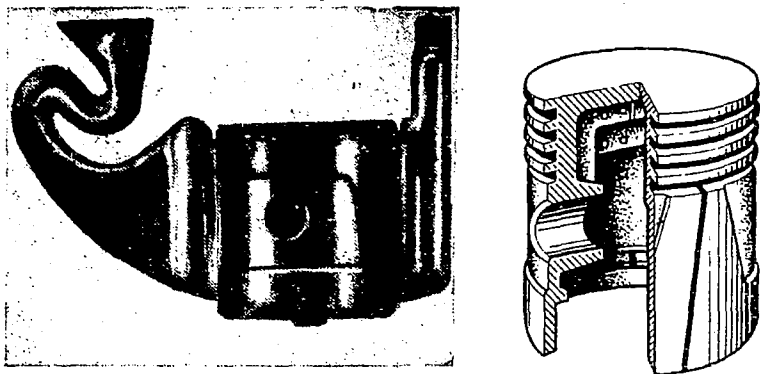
Автомобильный поршень. Слева — отливка, справа — готовый поршень (в разрезе)
